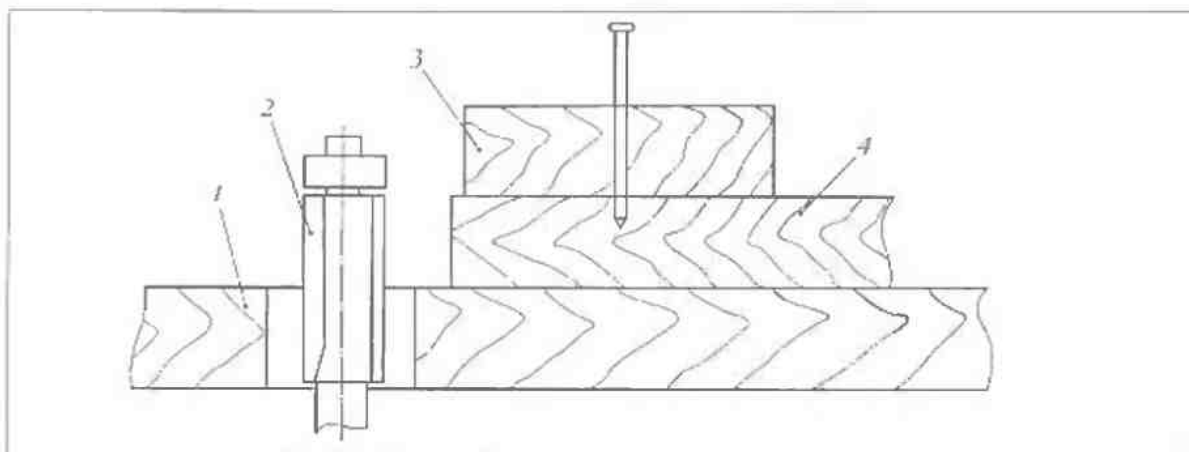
Фрезерование кромок деталей по контуру с помощью шаблона: 1 – рабочий стол; 2 – проходная фреза с подшипником; 3 – шаблон (линейка); 4 – обрабатываемая деталь
